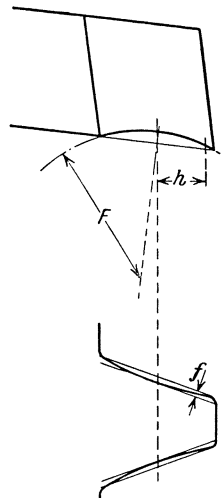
Korrigiertes zahnstangenartiges Werkzeug.
